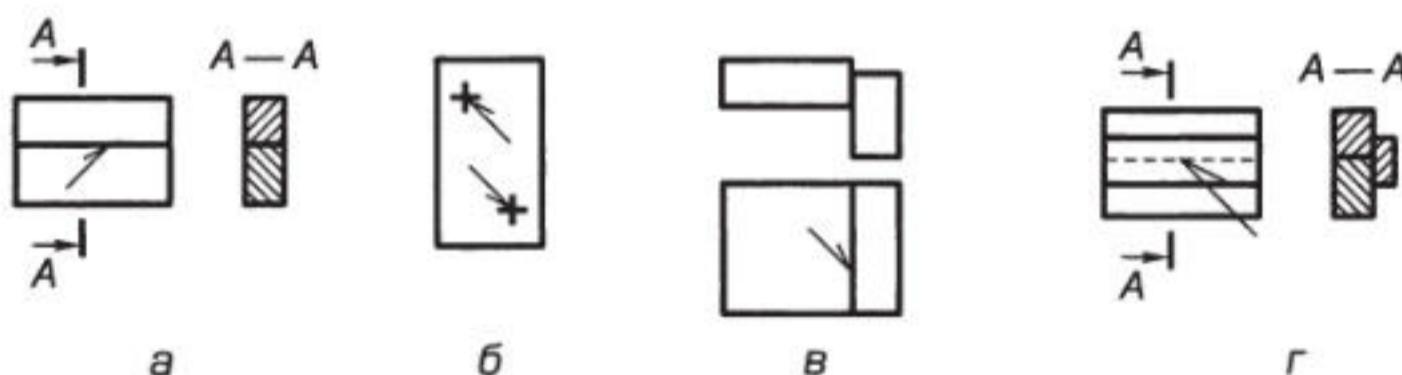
Условные изображения швов сварных соединений независимо от способа сварки
